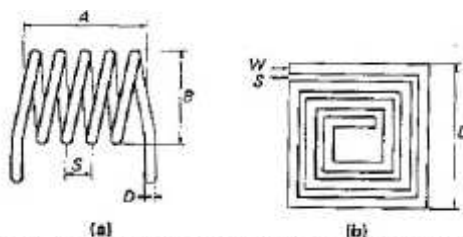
a) Bobina con núcleo de aire; b) Bobina impresa.
